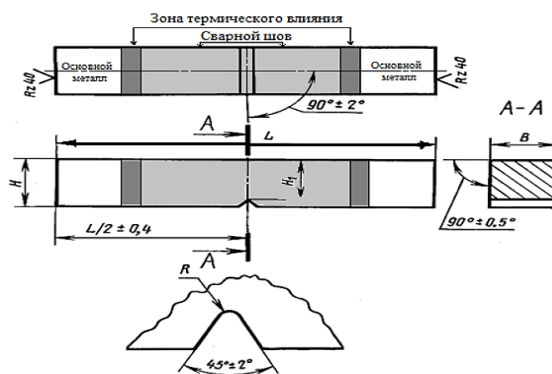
Образец из металла сварного шва для испытаний на ударный изгиб.
